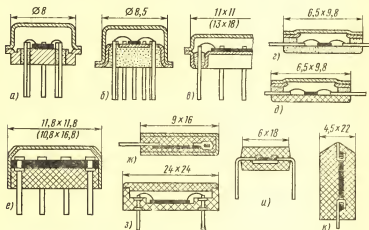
Схемы конструкций корпусов микросхем: а, б, в — металлостеклянных; г — стеклянного; д — керамического; е, ж — металлополимерных; з — пластмассового; и, к — полимерных
